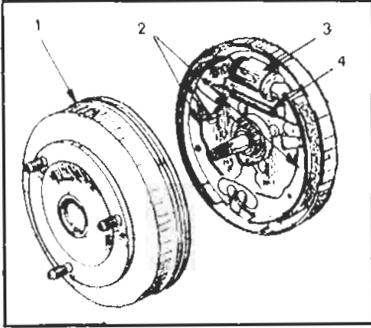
Disposición real de los elementos en un freno de zapatas. 1.- Tambor. 2.- Zapatas. 3.- Bombín. 4.- Muelle.
